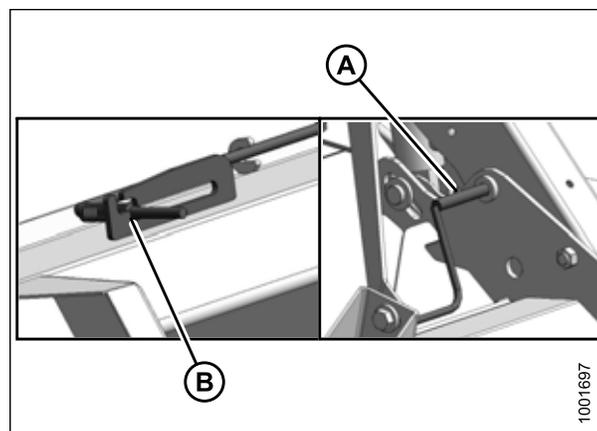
Предохранительный упор подбирающего мотовила — центральный рычаг
